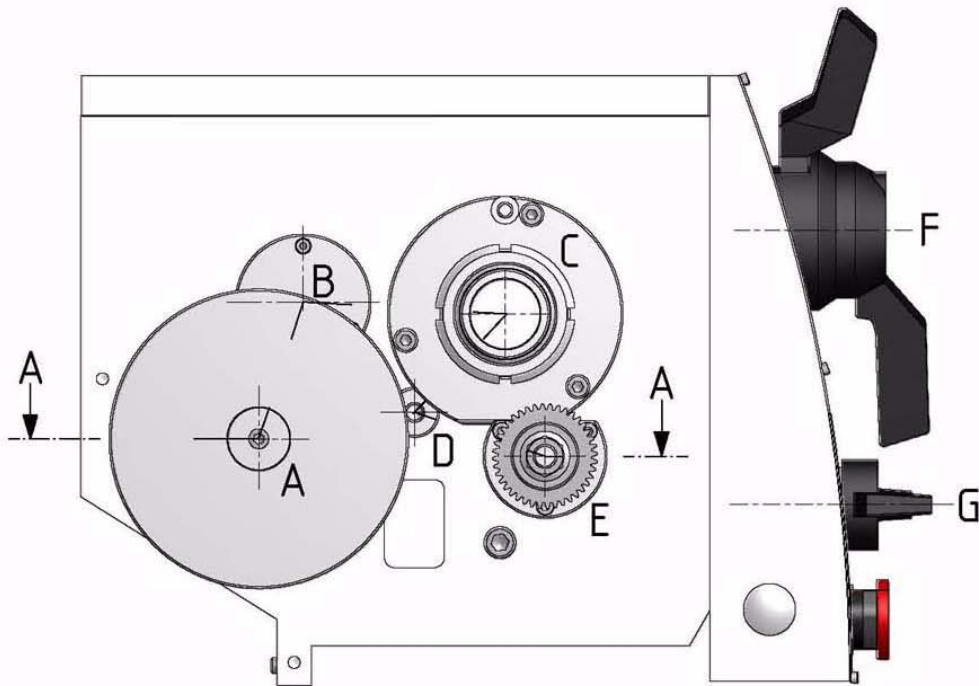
Getriebe Spindelstock 2-6 - Headstock gear 2-6
